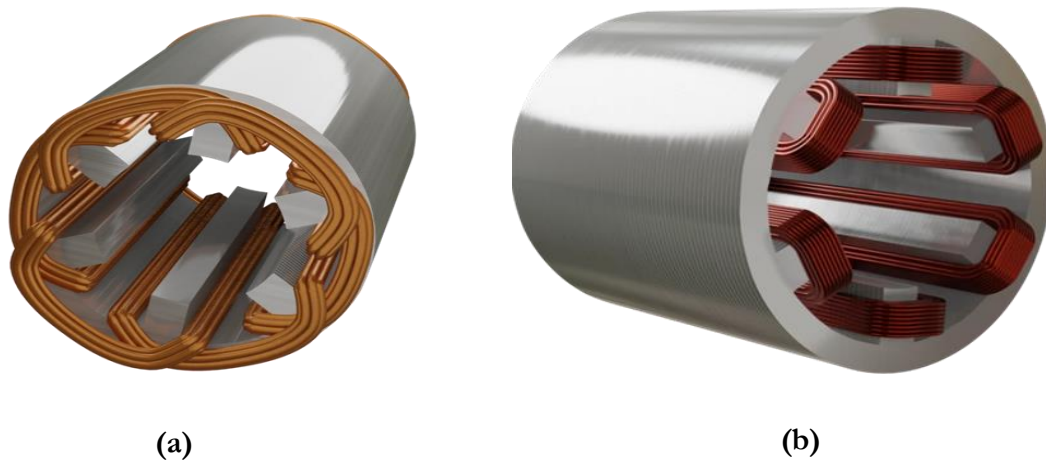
Bobinage d'une machine tournante, (a) : distribué ; (b) concentré
